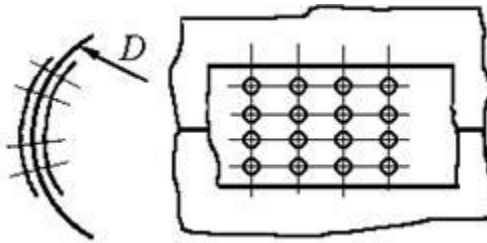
Заклепувальні шви циліндричного автоклава
